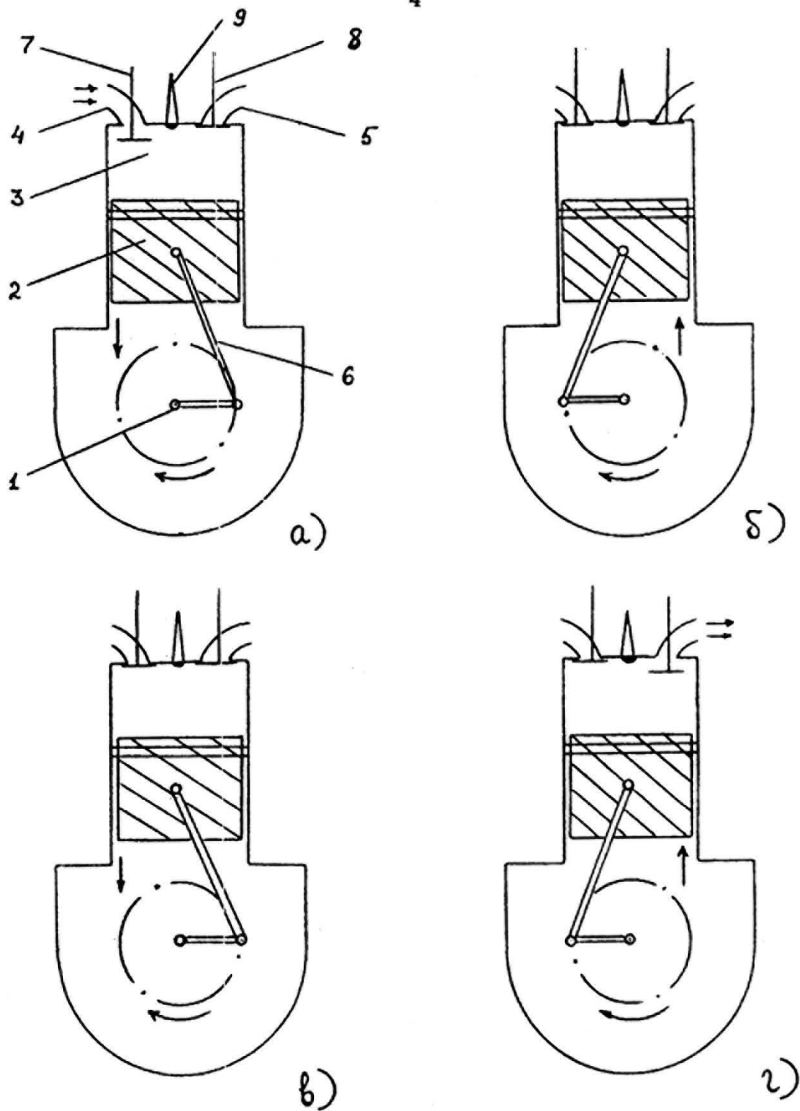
Схема работы четырехтактного одноцилиндрового карбюраторного двигателя.
